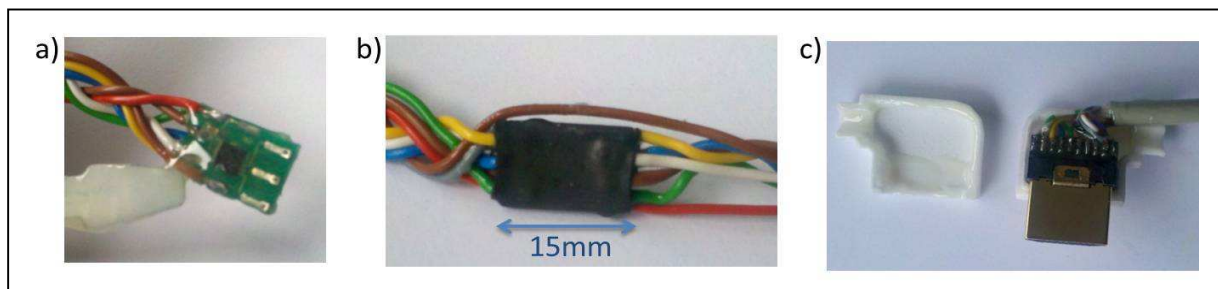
a) Die Sensor-Platine wird mit einer Zweikomponentenkleber verkapselt. b) Ein Schrumpfschlauch schützt zusätzlich die Sensor-Platine. c) Der HDMI Stecker wird in ein dafür konstruiertes Gehäuse verkapselt.
